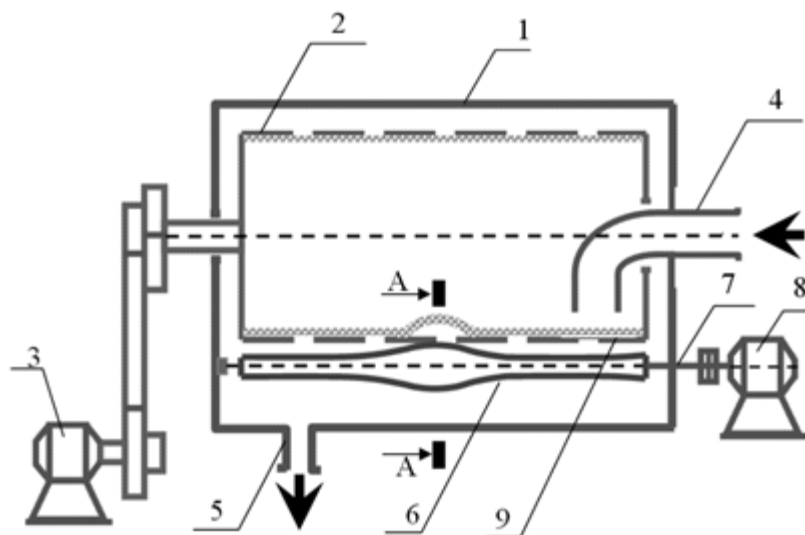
Общий вид конструкции фильтрующей центрифуги
